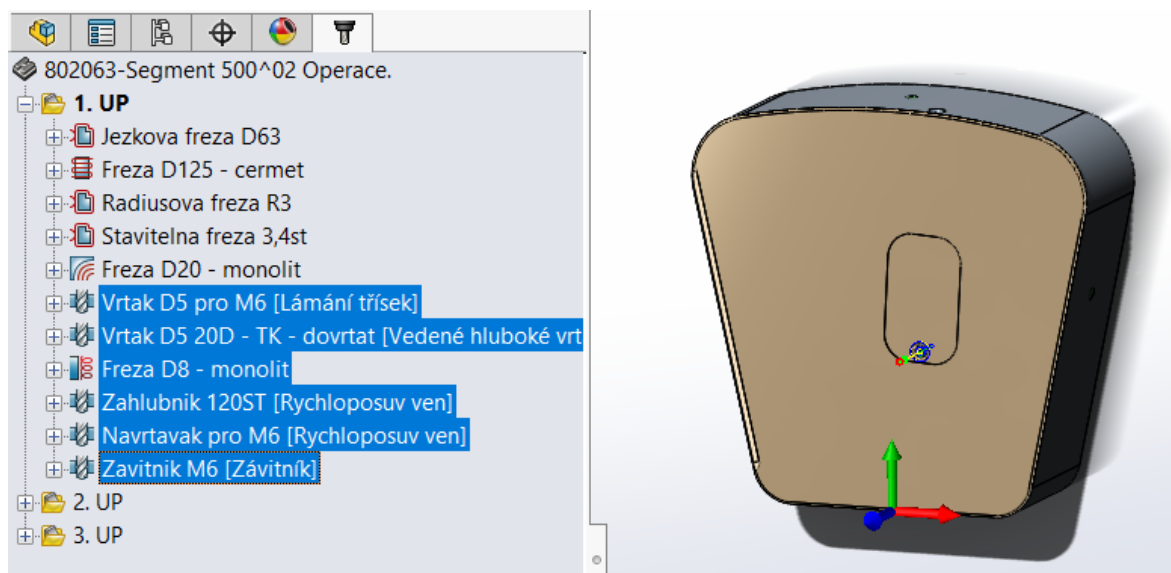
Nástroj operace Fréza D20 – monolit [10]
